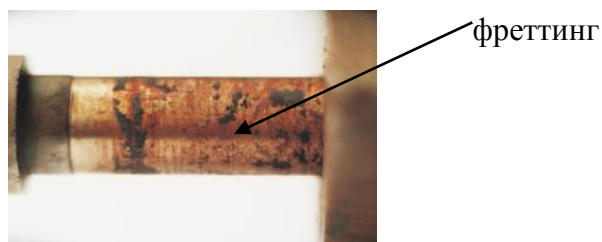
Пример фреттинга на оси шарнирного соединения.
